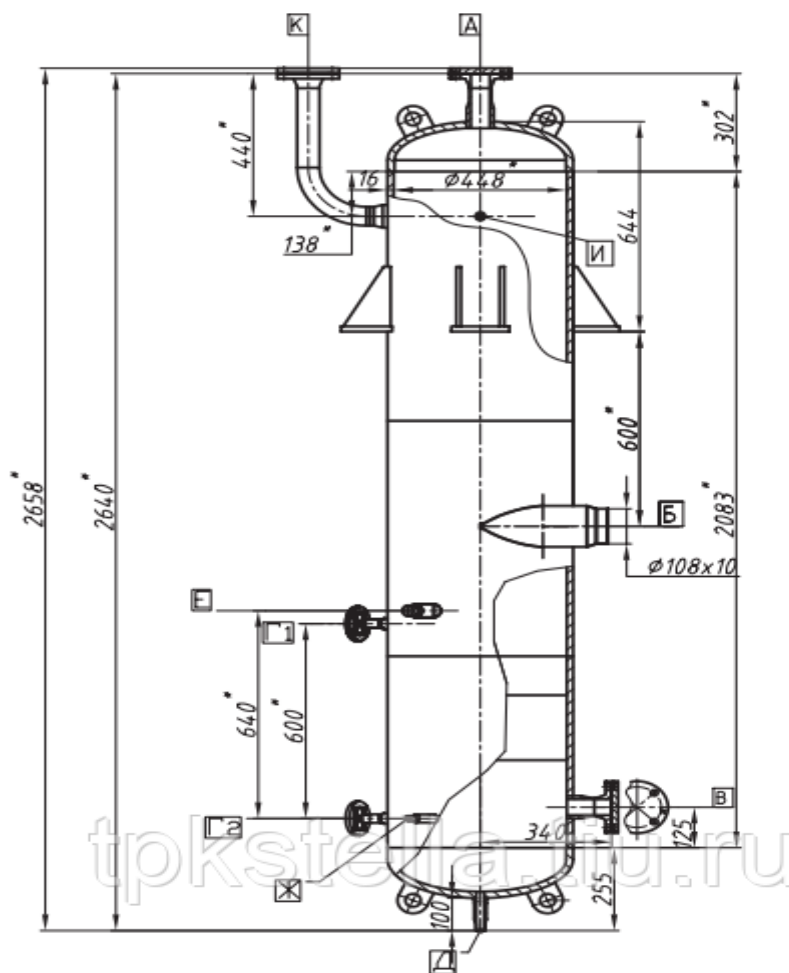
Габаритный чертёж расширителя непрерывной продувки РП-0,4-0,44
